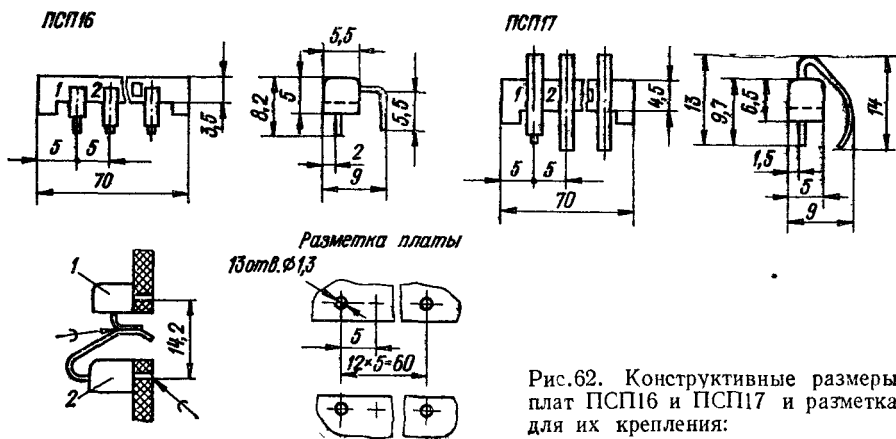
Конструктивные размеры плат ПСП16 и ПСП17 и разметка для их крепления:
